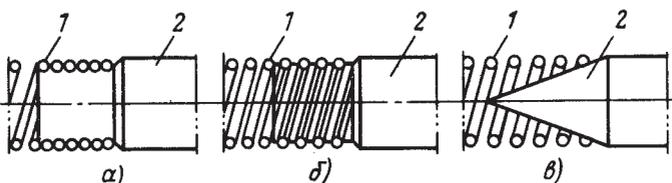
Способы соединения спирали нагревательного элемента с контактным стержнем, внутренний конец которого имеет цилиндрическую (а), резьбовую (б) и коническую (в) поверхности:
